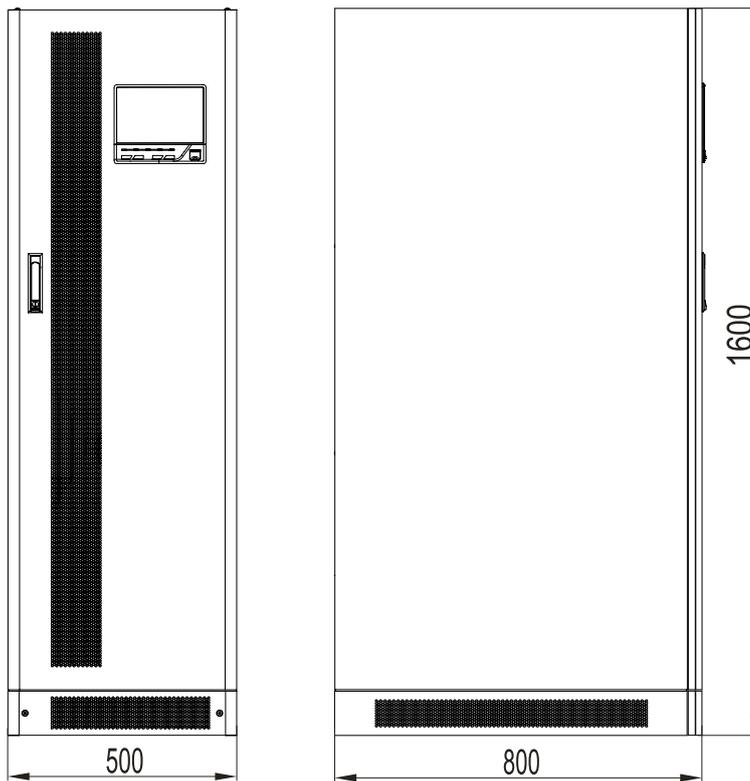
Размеры для FR-UK(/B)33(40-80)
